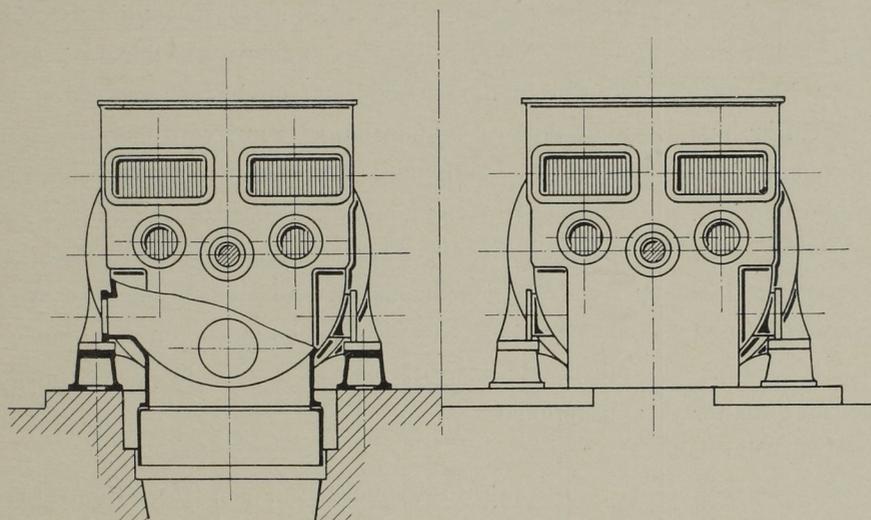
Stirnansicht der Gebläsecylinder. Massst. 1:60.
